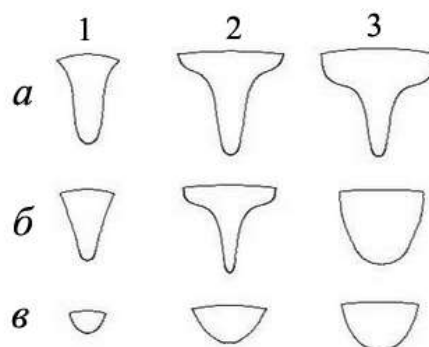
Форми зварного шва за різної потужності лазера дуги:
